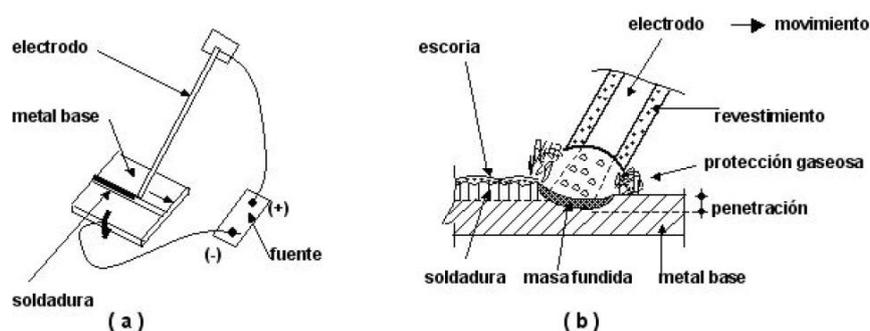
Soldadura por arco eléctrico con aporte de material. Fuente: Libro Est. Metálicas – G. Troglia
